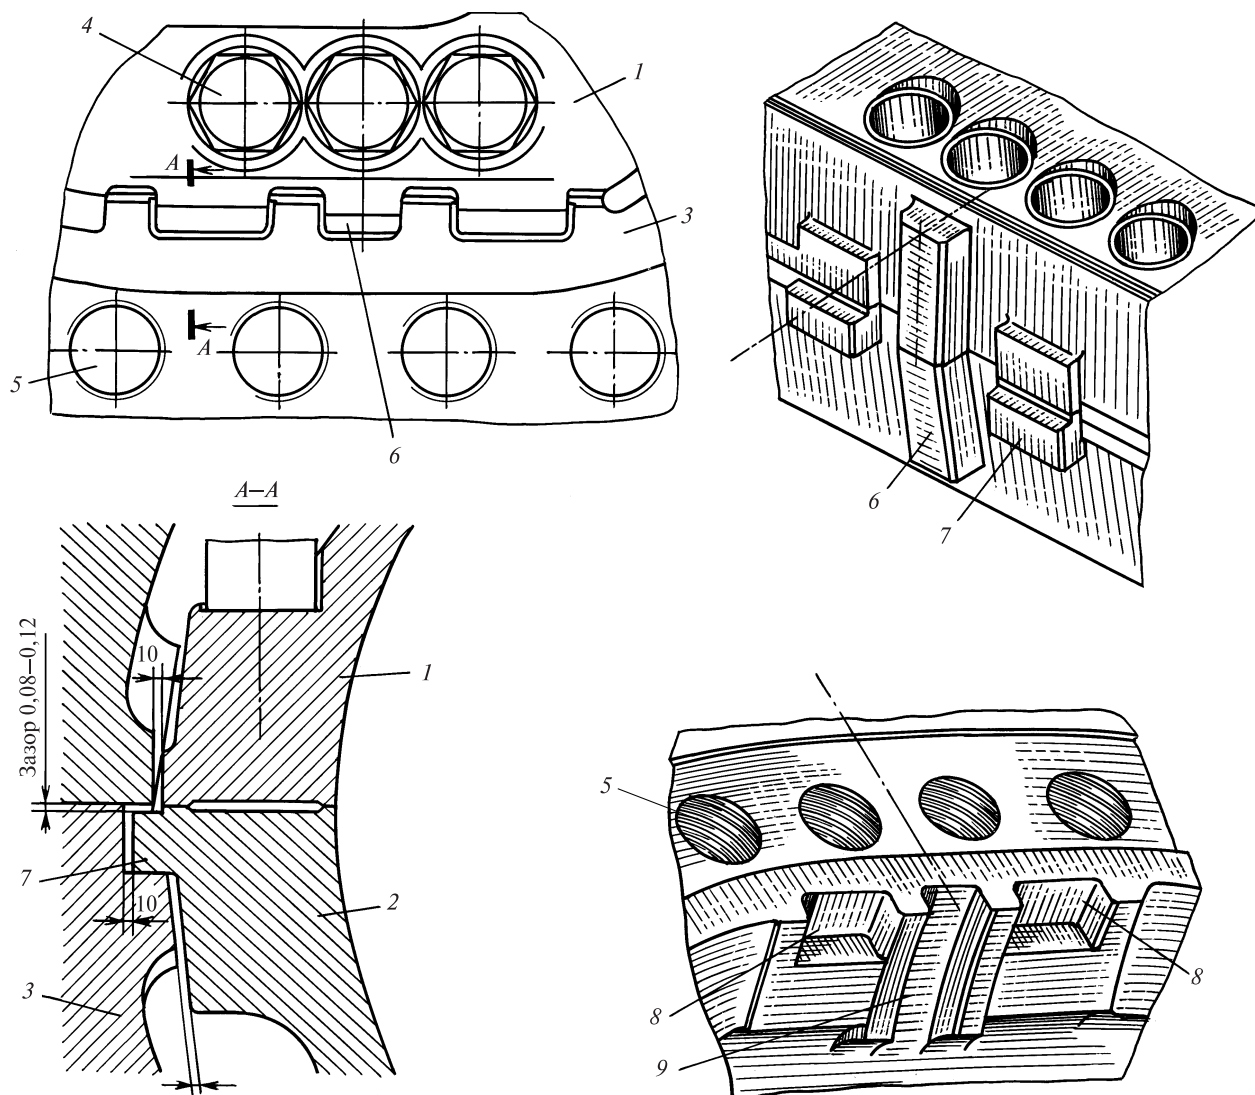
Детали подвески внутреннего корпуса двухстенного ЦВД во внешнем корпусе
